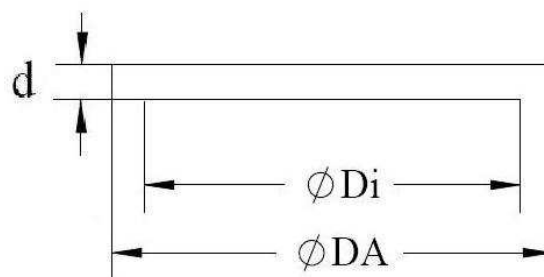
Zylindrische Form des Mantels von Thermomessfühler
